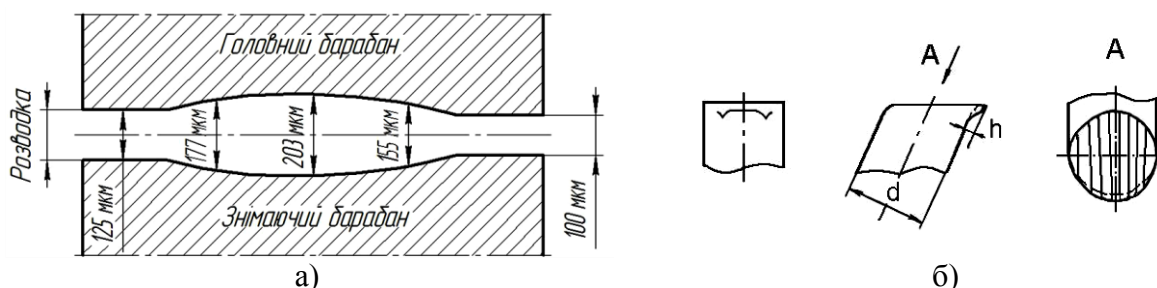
Похибка форми твірних барабанів а) та робочої поверхні голки б)
